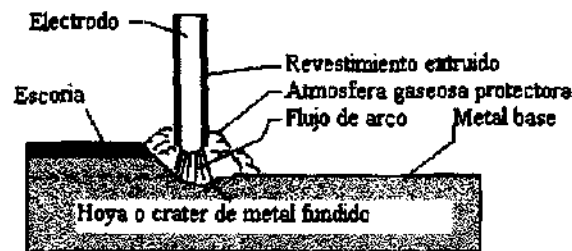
Elementos del proceso de soldadura de arco metálico protegido.
